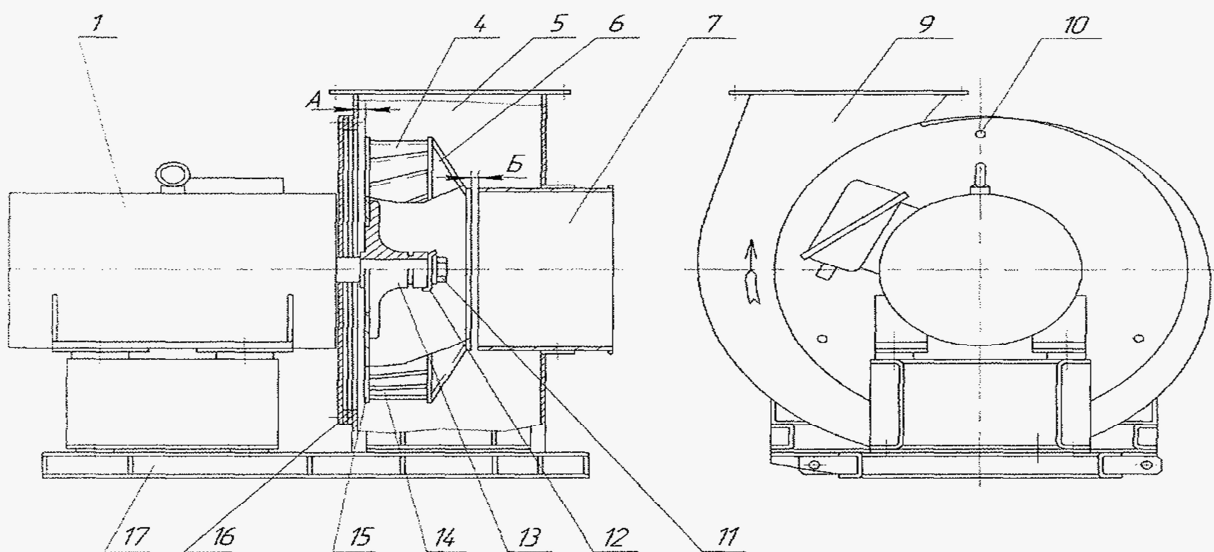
Блок центробежного вентилятора Ц9-37,6-7,6
